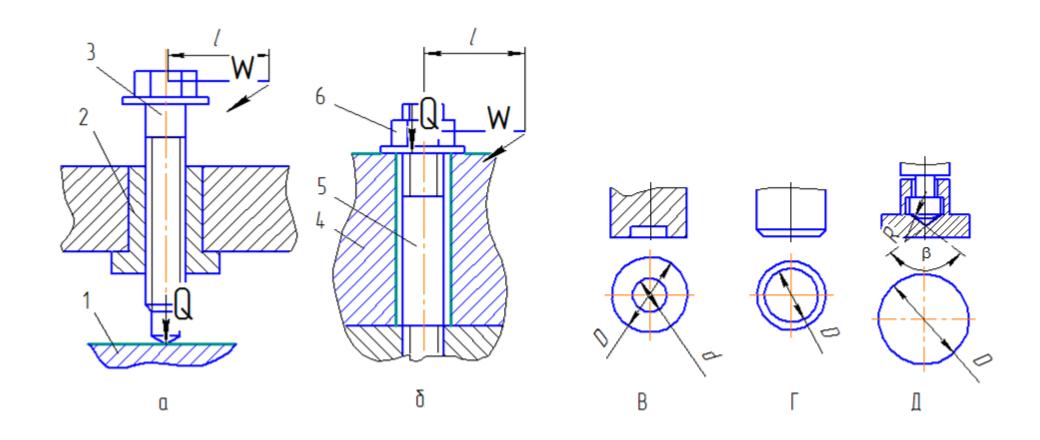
Конструкции винтовых зажимов: 1, 4 — заготовка; 2 — втулка резьбовая; 3 — винт; 5 — шпилька; 6 - гайка
